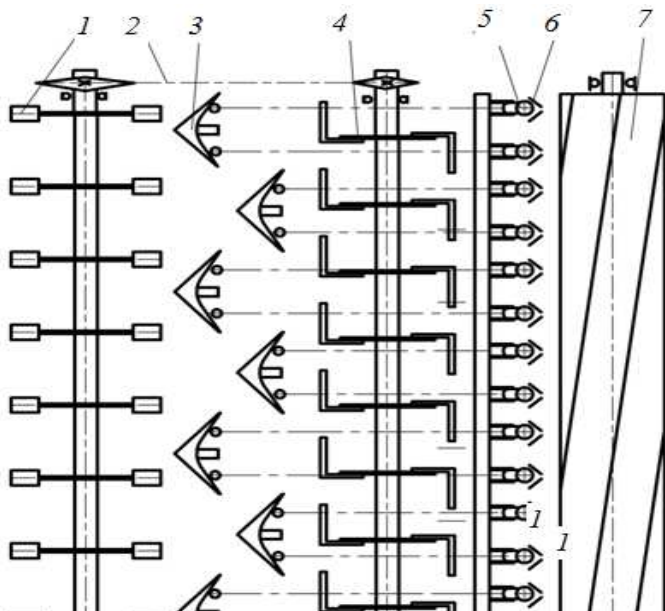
Агрегат для предпосевной обработки почвы и посева (схема размещения рабочих органов):
